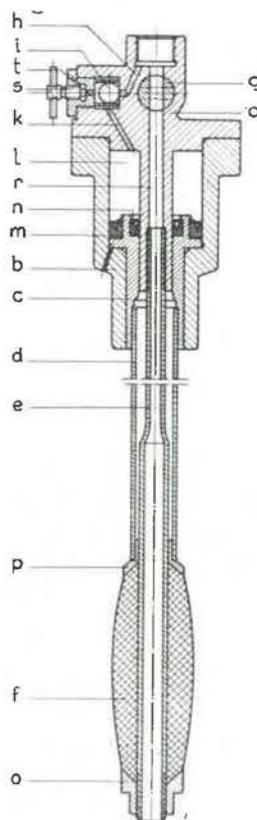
Coupe de la canne d'injection d'eau en veine Hausherr à serrage automatique des joints de caoutchouc.
